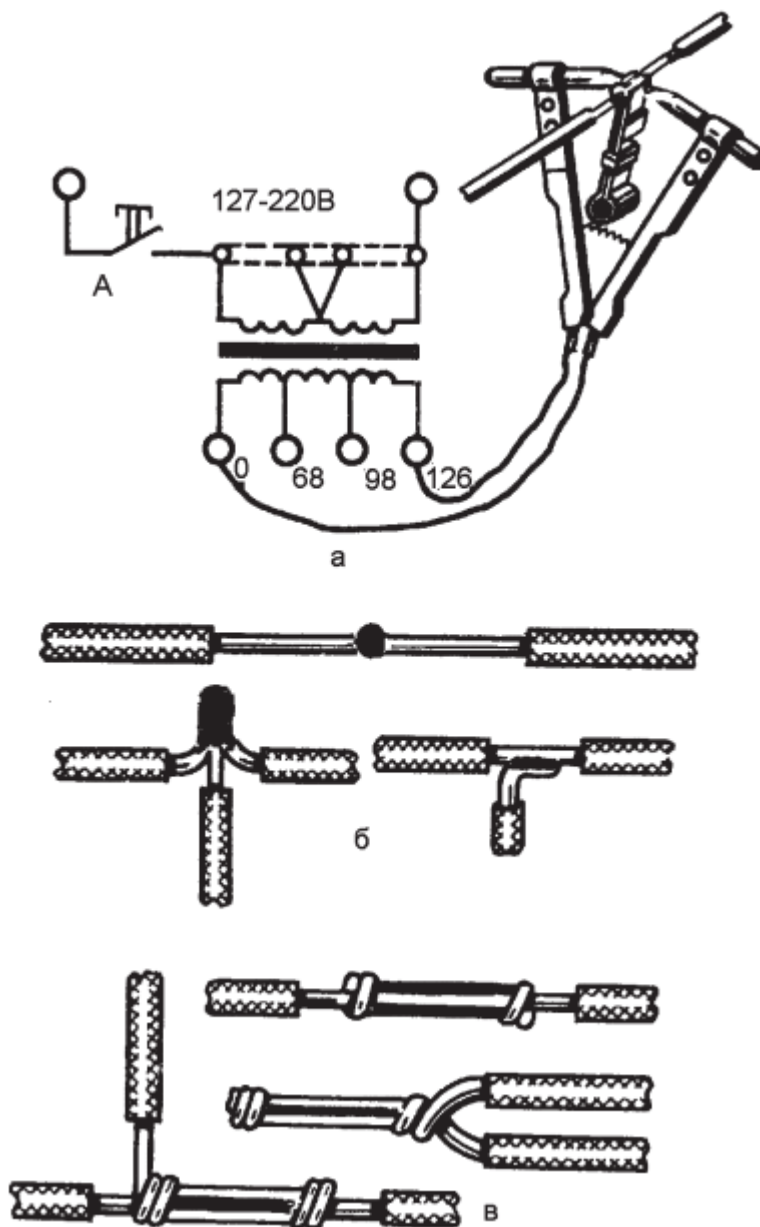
Соединение проводов сваркой и пайкой: а – соединение однопроволочных алюминиевых проводов сваркой в гильзе; б – образцы сварок; в – соединение пайкой
